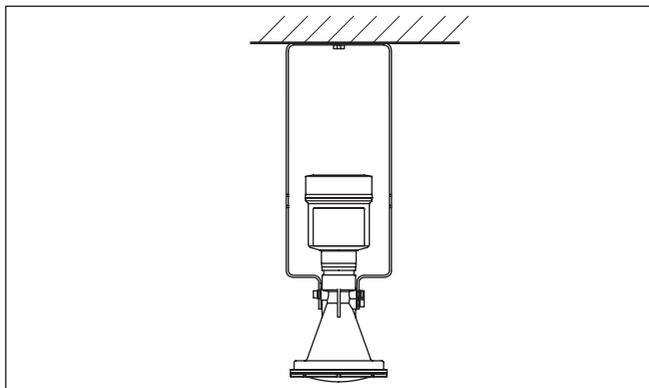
Монтаж на перекрытии на монтажной скобе длиной 300 мм
